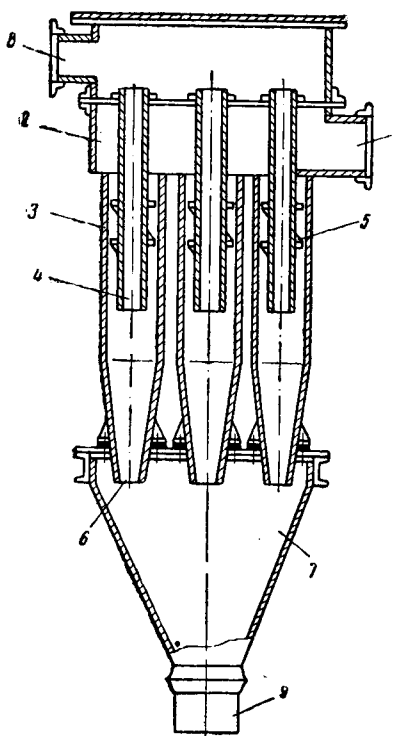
Батарейный циклон «Винт»: 1 — входной патрубок; 2 — распределительная камера; 3 — корпус элемента; 4 — выхлопные трубы; 5 — направляющие аппараты; 6 — пылеотводящие отверстия; 7 — бункер; 8 — камера для очищенного газа; 9 — точка
